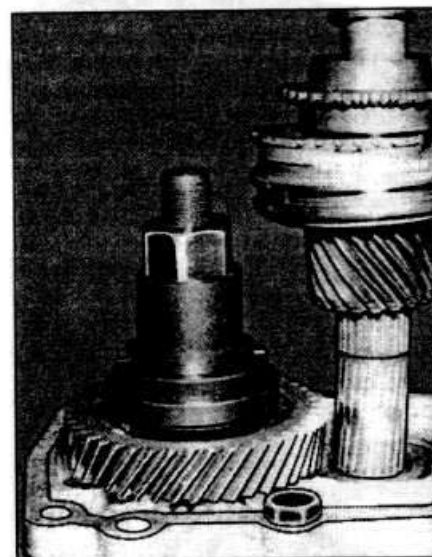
Установка съемника 16.033 для спрессовки шестерни V передачи
